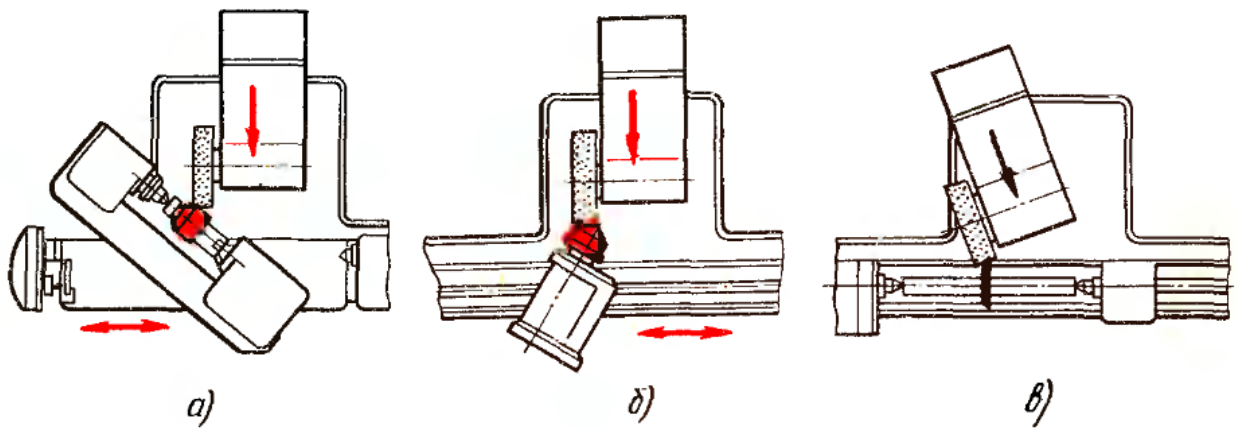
Схема наладки станка для шлифования поверхности с большой конусностью
